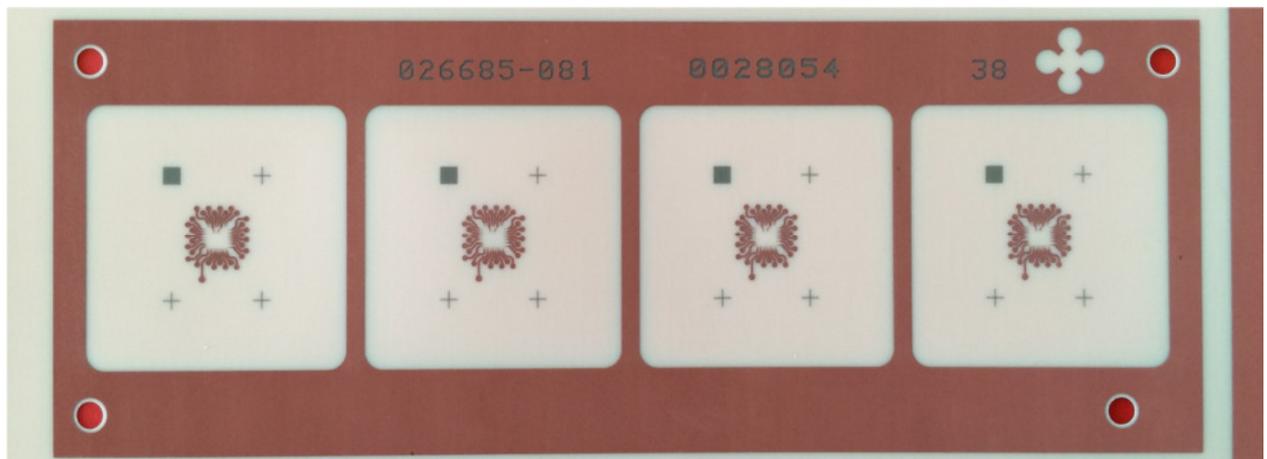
Interposer Layout für den Embedding Demonstrator (ohne passive Komponenten)
